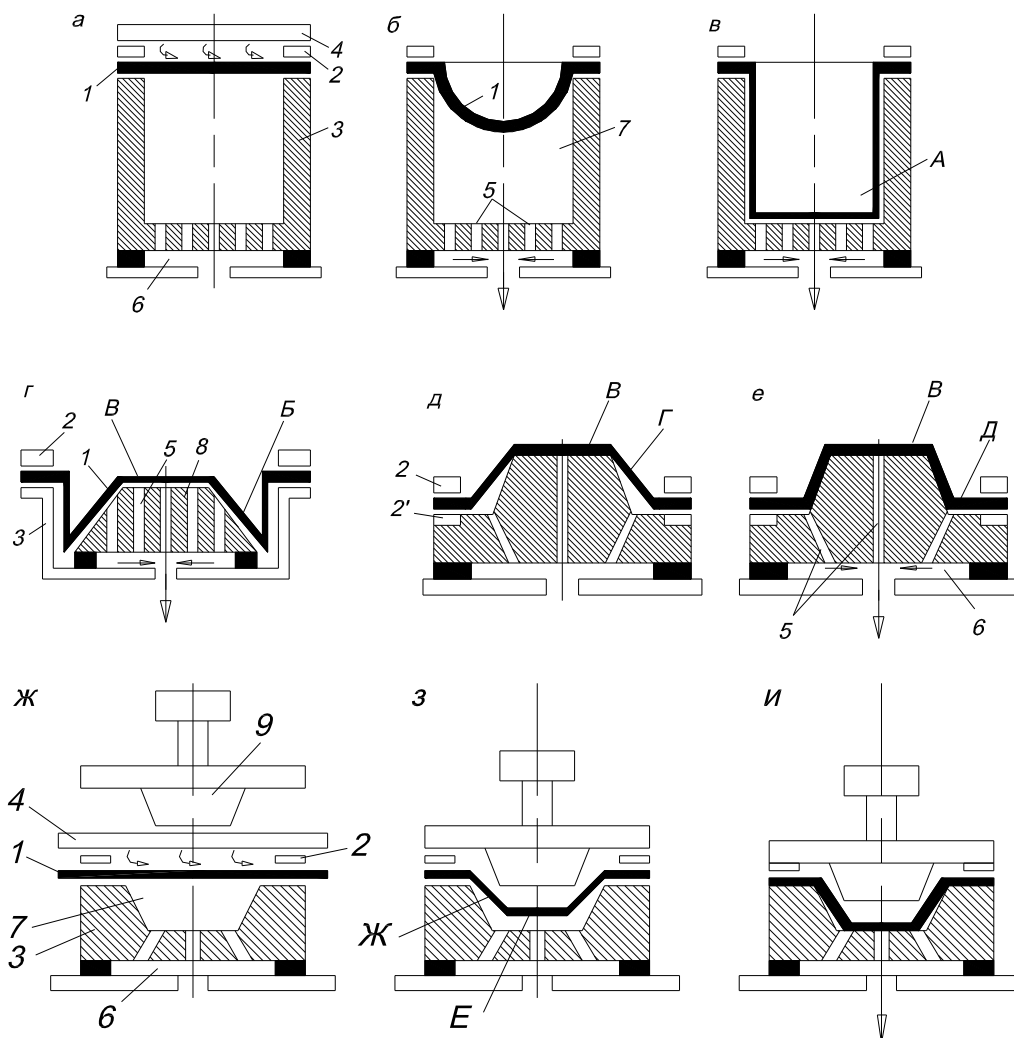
Різновиди пневмовакуумформування: а–в – негативне формування; г – позитивне формування; д, е – позитивне формування з попередньою механічною витяжкою; ж–и – негативне формування з попередньою механічною витяжкою (1 – формований лист; 2 – притискна рама; 3 – матриця; 4 – нагрівник; 5 – вентиляційні канали; 6 – вакуумна порожнина матриці; 7 – формуюча порожнина; 8 – пуансон)
